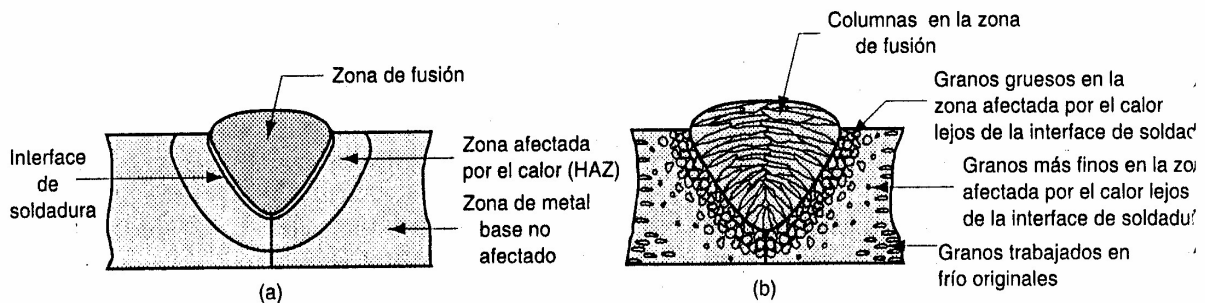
Sección transversal de una junta soldada por fusión común.
